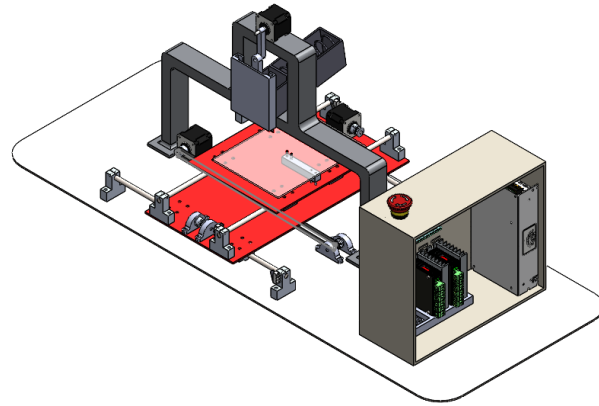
Vista isométrica del ensamblaje posicionada de champiñón.
